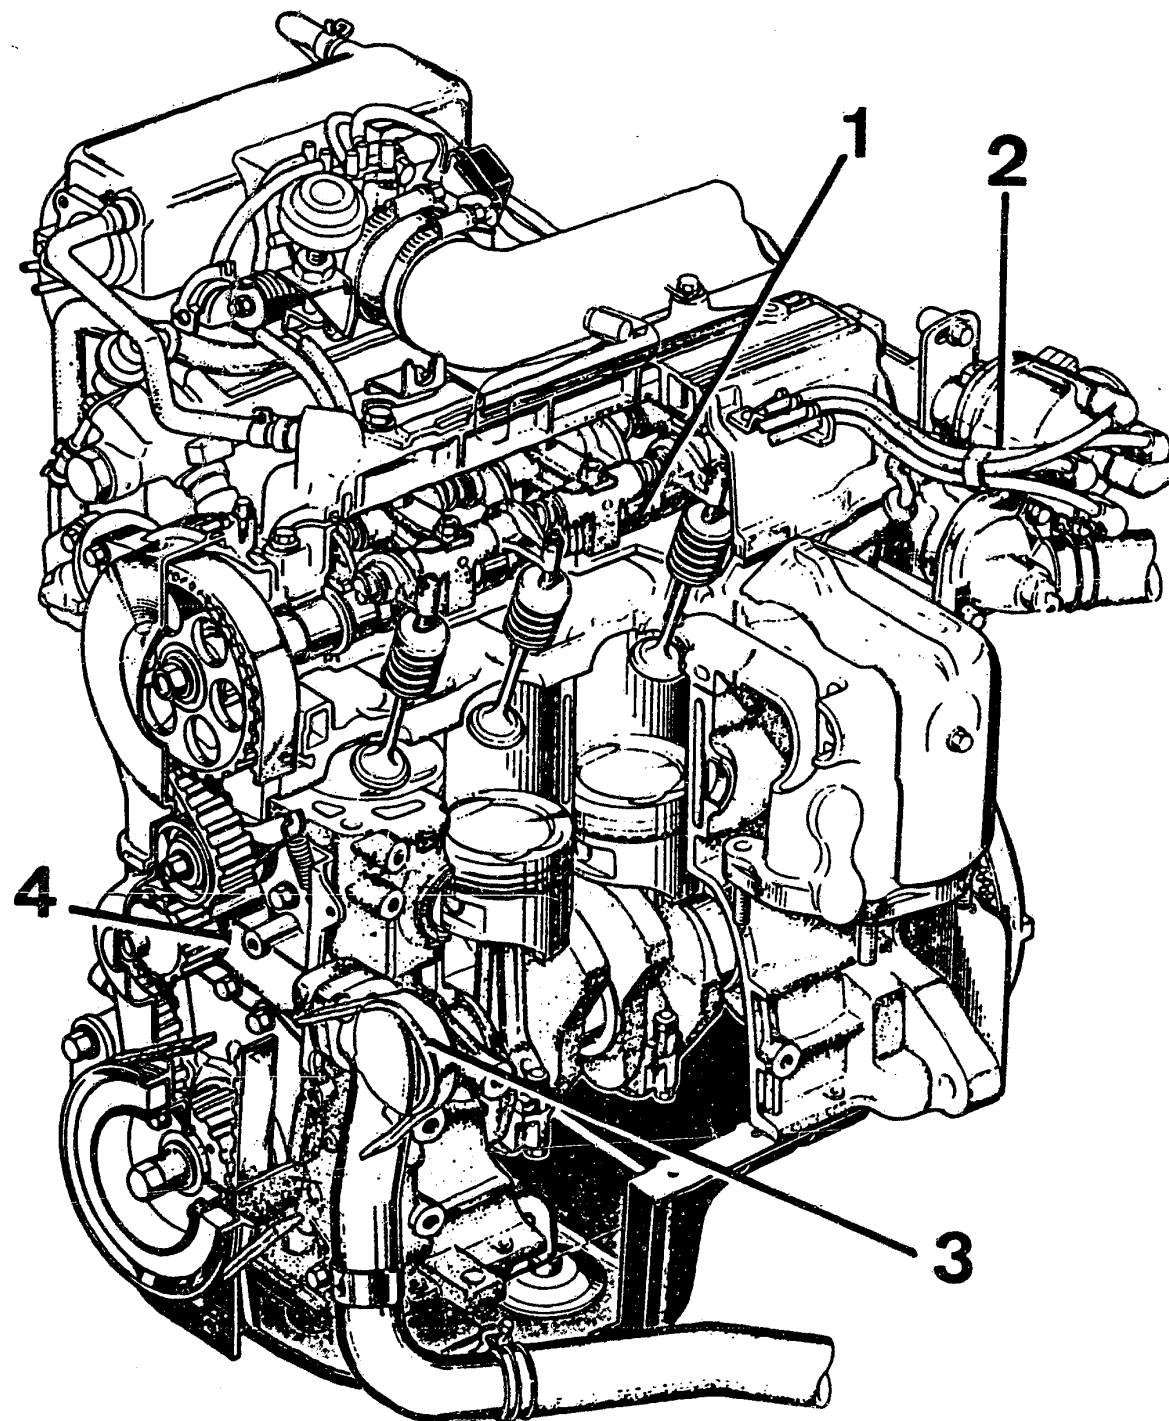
Teilschnittbild durch den 2,0 l-Motor FE mit der Einspritzanlage EGI. 1 Nockenwelle – 2 Zündverteiler – 3 Hydraulikpumpe – 4 Wasserpumpe.
